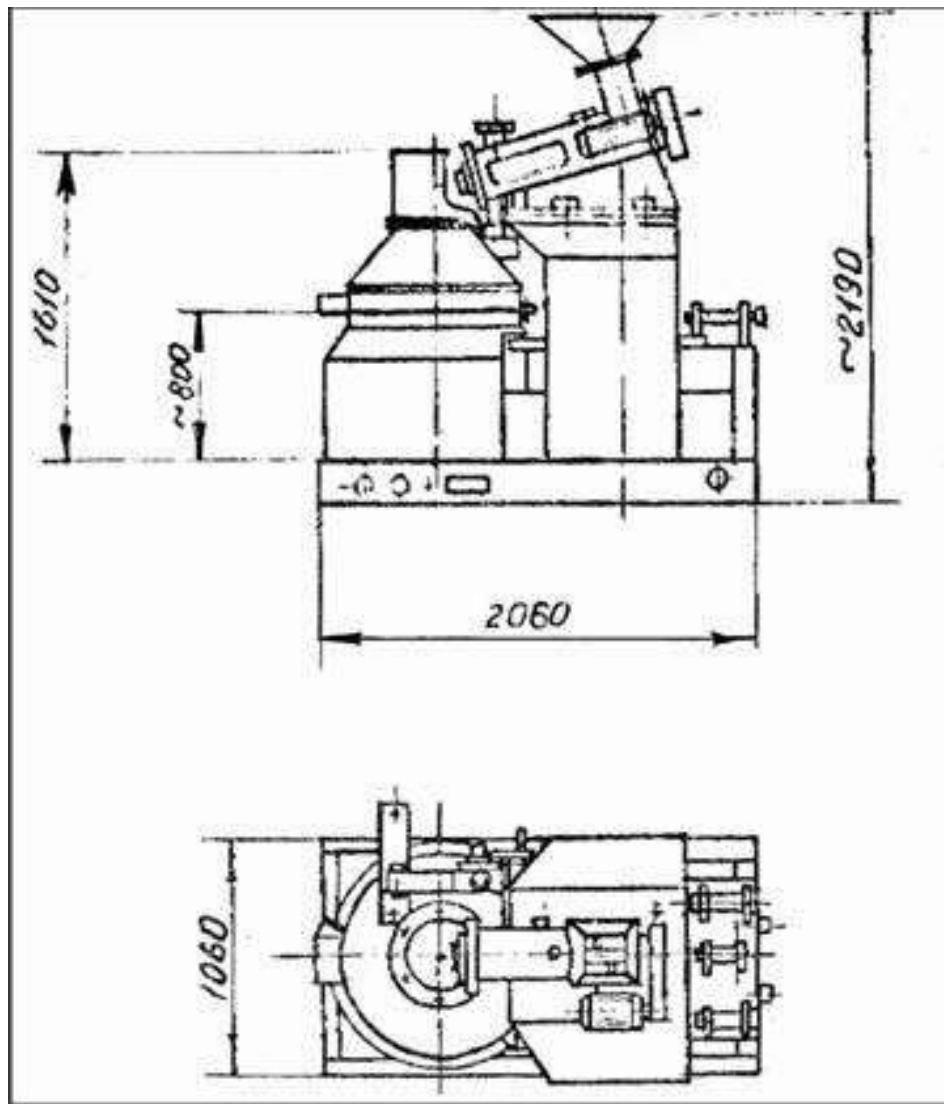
Прес-гранулятор одновалковий Е 8-ДГЖ
